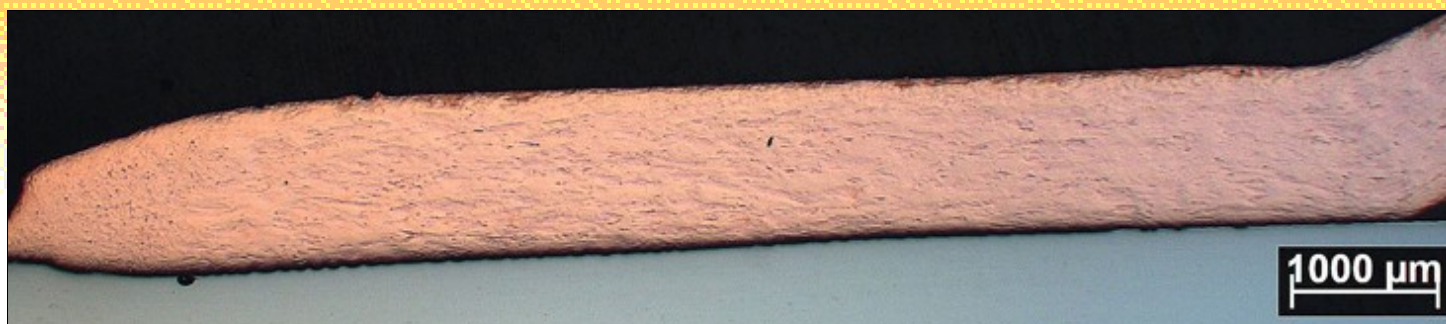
interface d'une soudure cuivre/acier inoxydable (x12)
